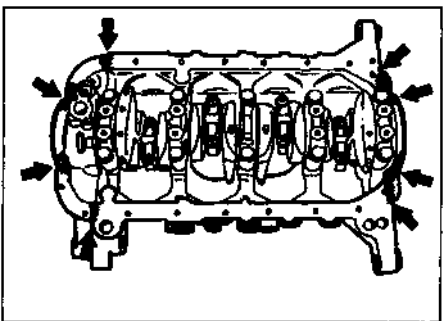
,в. Выверните болты картера коренных опор...
